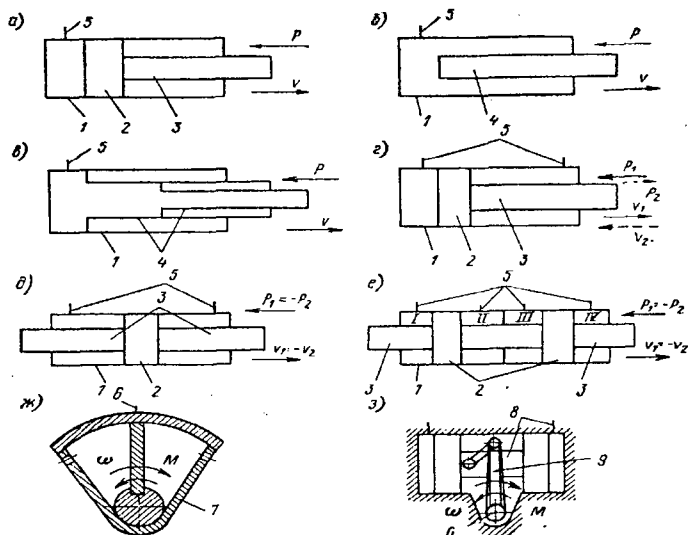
Гидродвигатели возвратно-поступательного и поворотного движения. Гидроцилиндры: а – поршневой одинарного действия; б – плунжерный; в – телескопический; г – двойного действия; д – с двусторонним штоком; е – со сдвоенными поршнями; ж и з – поворотники
